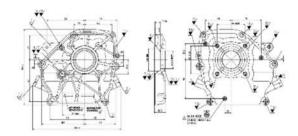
Layout baru fixture untuk produk cover crankcase dan cylinder head
